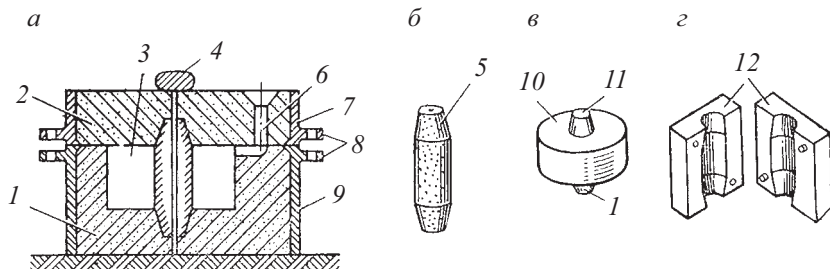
Литейная форма (*а*), стержень (*б*), модель (*в*), стержневой ящик (*г*) для получения отливки зубчатого колеса
